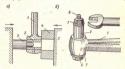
Выпрессовка и запрессовка втулки верхией головки шатуна с помощью:
